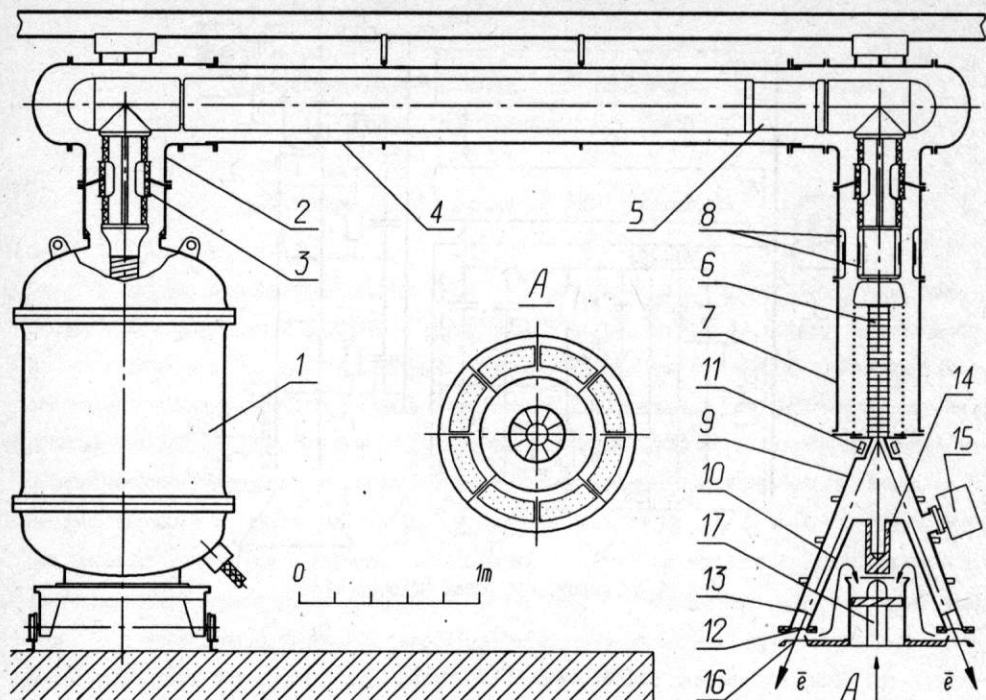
Конструкция ускорителя: 1 - источник высокого напряжения; 2 - угловой переход; 3 - проходной электроввод; 4 - коаксиал; 5 - резистор ограничительный; 6 - трубка ускорительная; 7 - корпус трубки; 8 - трансформатор накальный; 9 - конус развертки наружный; 10 - конус развертки внутренний; 11 - электромагниты кольцевой развертки; 12 - выпускное окно; 13 - защитные полоски фольги; 14 - цилиндр Фарадея; 15 - вакуумный насос; 16 - окно защитное; 17 - вентилятор
